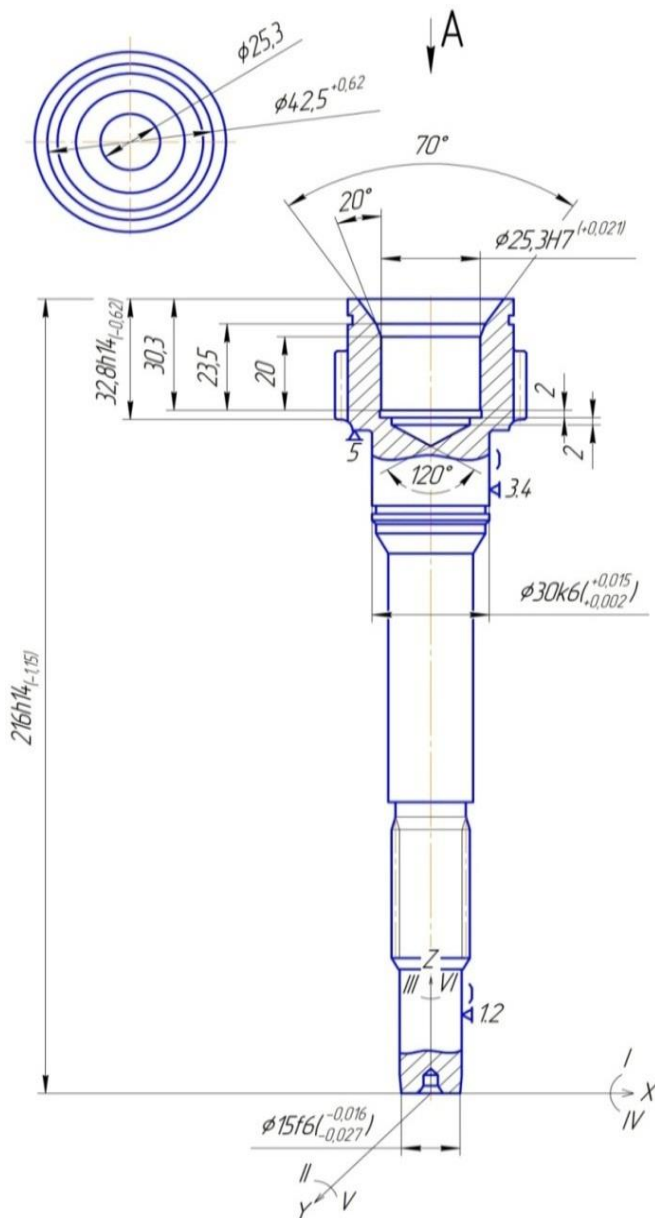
Схема базування заготовки в призмах (другий варіант)
